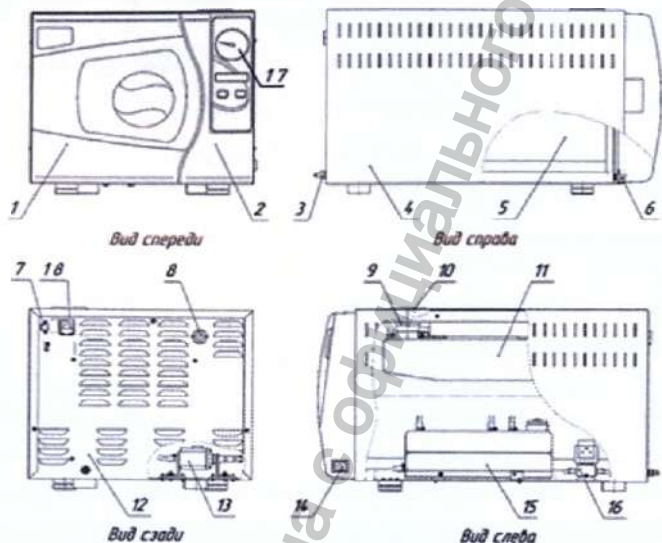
Внешний вид стерилизатора парового ГКа-25-ПЗ в варианте исполнения КИУС.942711.004-07.
